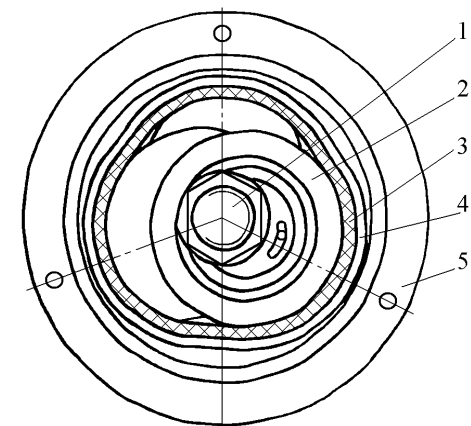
Общий вид трехволновой зубчатой передачи с металлополимерным гибким колесом:
